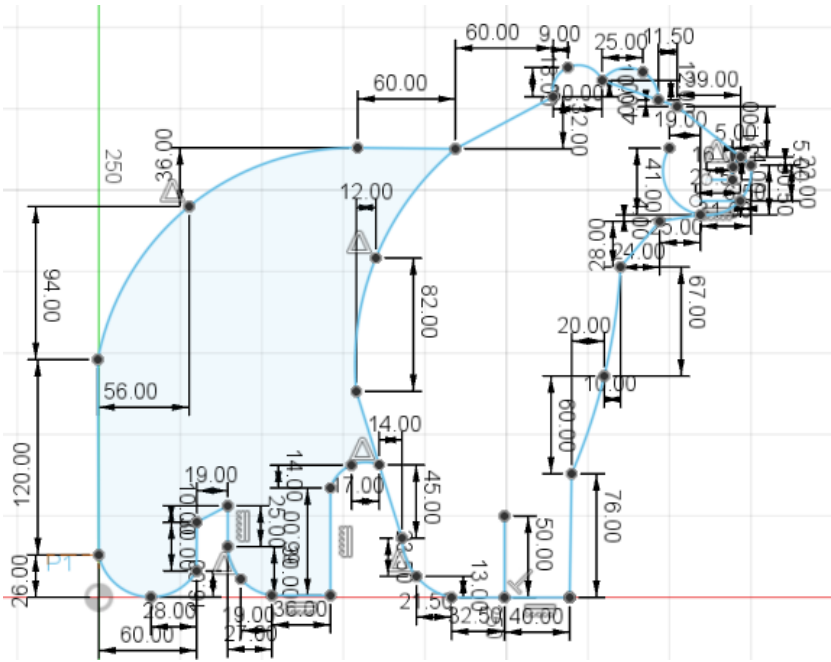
Urso cotado com dimensões e as *constraints* do desenho.
